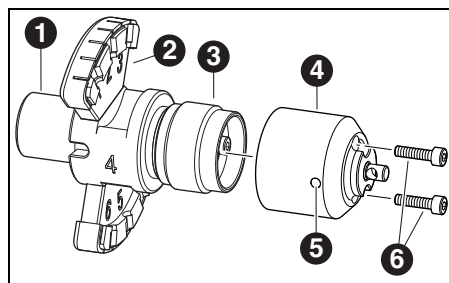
Bauteile Ceramill Werkstückhalter Rotationsfräsen
